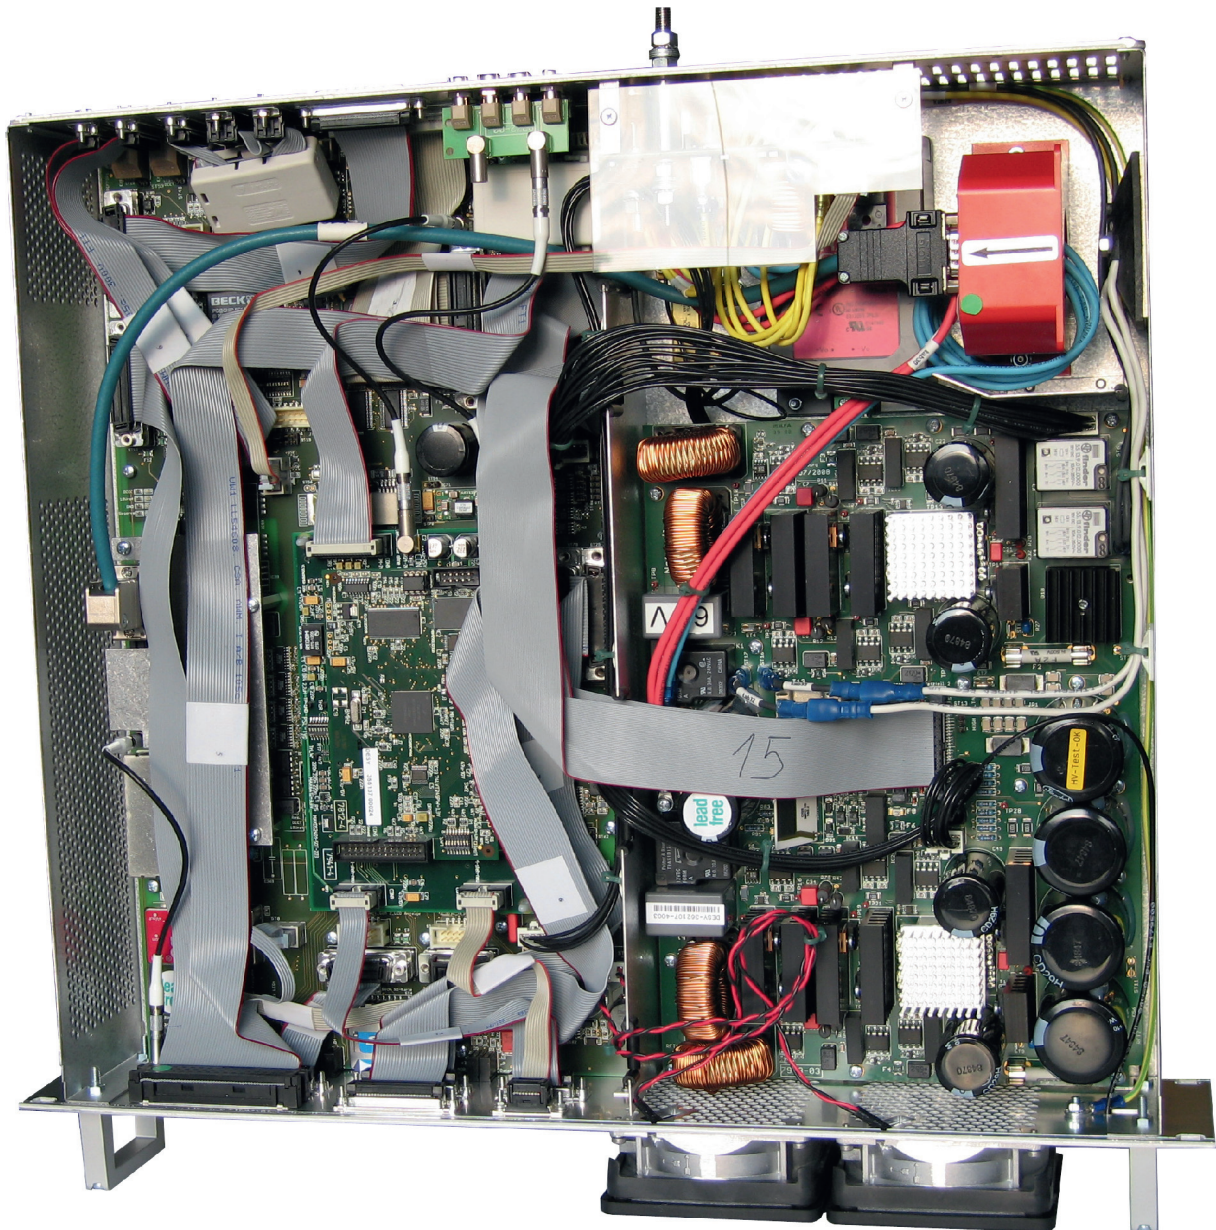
Sicht auf die einzelnen Baugruppen des Korrekturnetzteils – beim Regler für Choppernetzteile fehlt die rechte Baugruppe.
